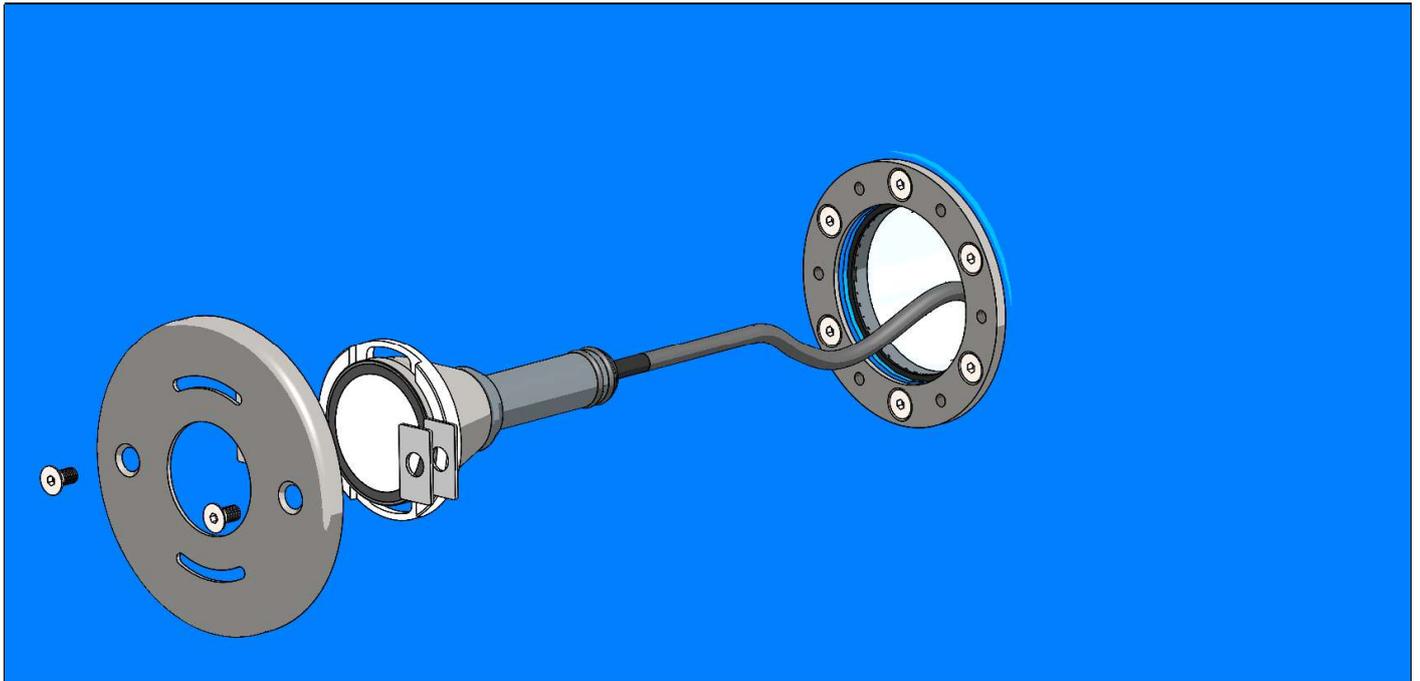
Kit di montaggio della piscina in cemento con pellicola sigillante
